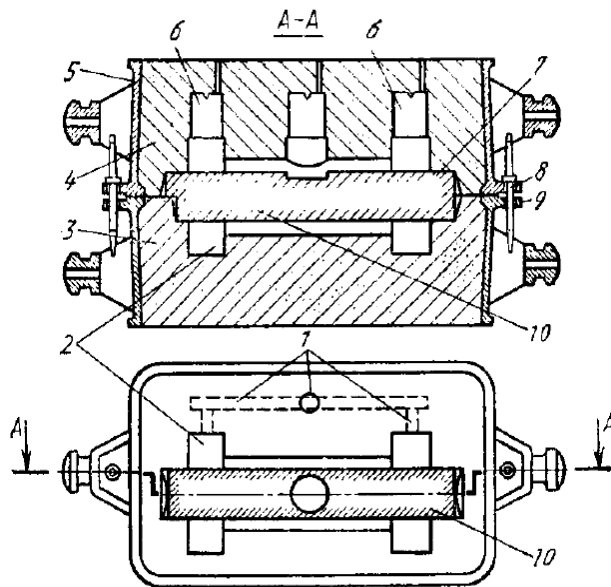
Литейная разовая песчаная форма: 1- литниковая система; 2- полость формы; 3- нижняя полуформа; 4- верхняя полуформа; 5- опока; 6- прибыли; 7- знаковая часть стержня; 8- штырь; 9- втулка; 10- стержень
